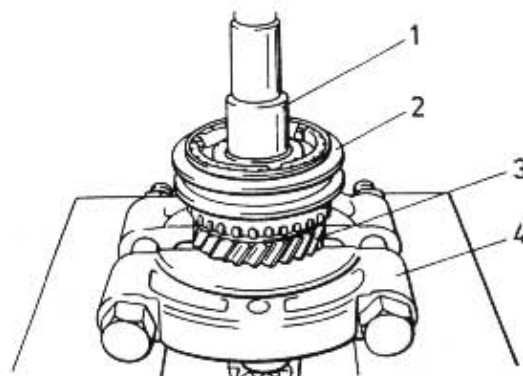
DEMONTAŻ ŁOŻYSKA TYLNEGO Z WAŁKA SPRZĘGLOWEGO
